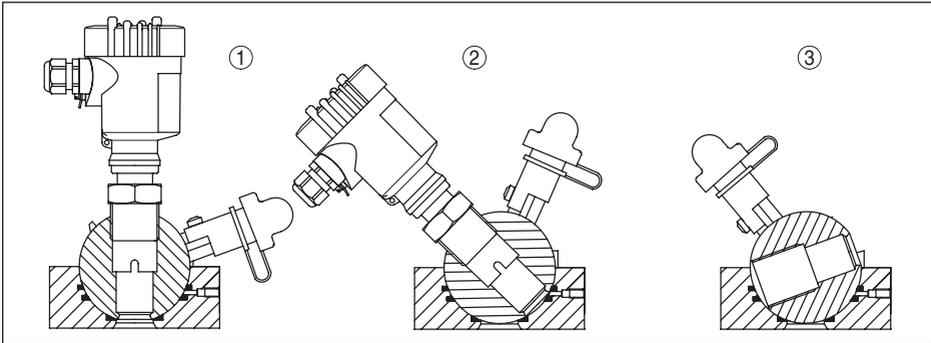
Posiciones de la conexión de la válvula de bola PASVE
